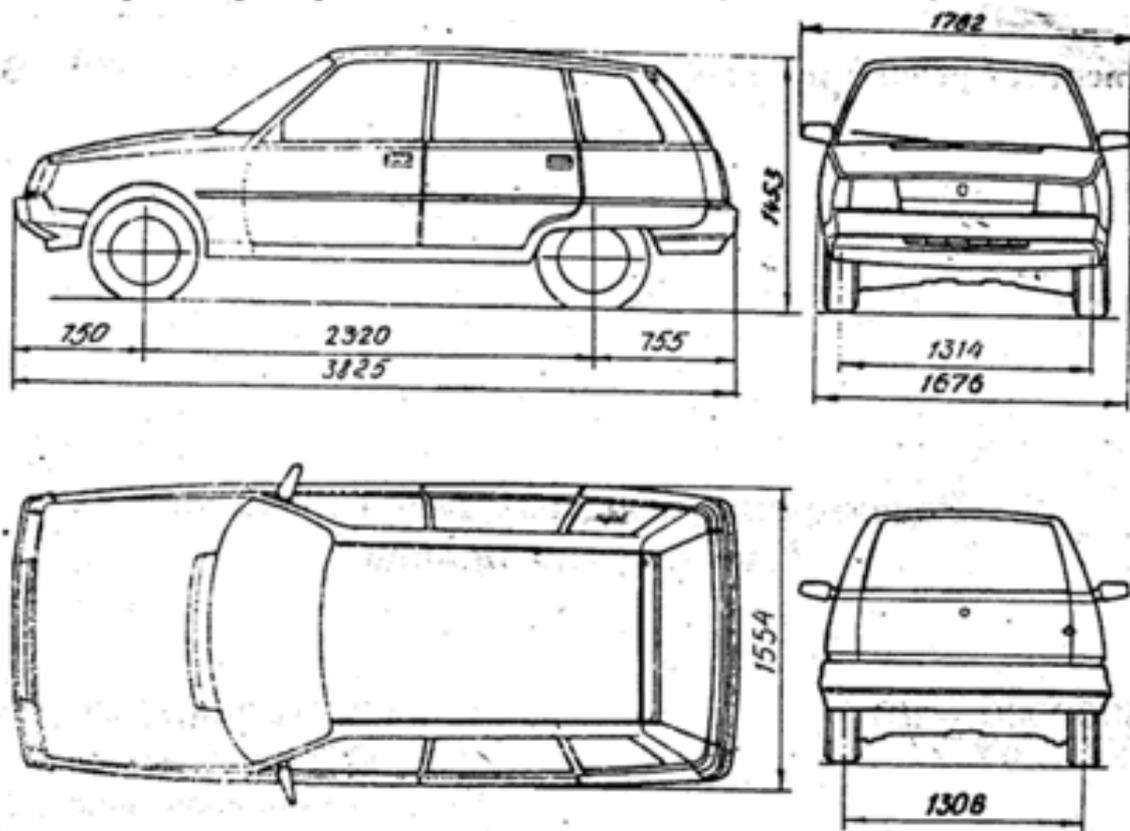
Основные габаритные размеры автомобилей ЗАЗ-1105 и ЗАЗ-1125 (высота без нагрузки)
